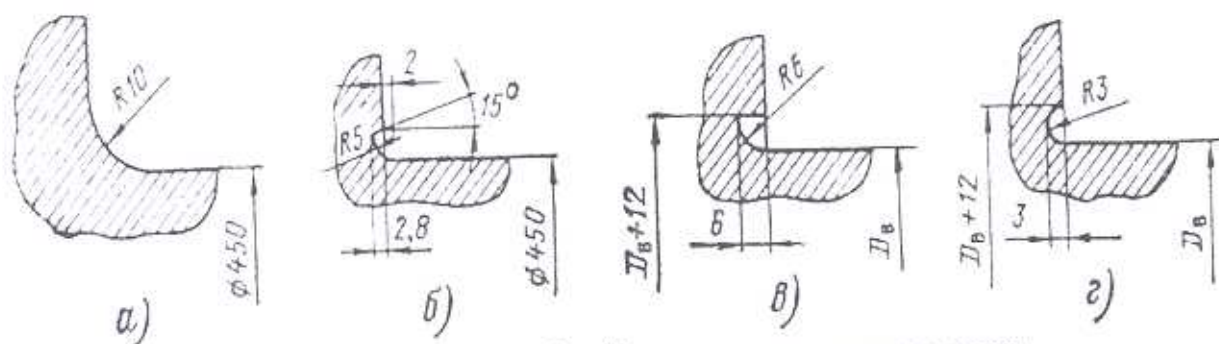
Сопряжение рабочей поверхности упорного диска и поверхности вала [1]:
